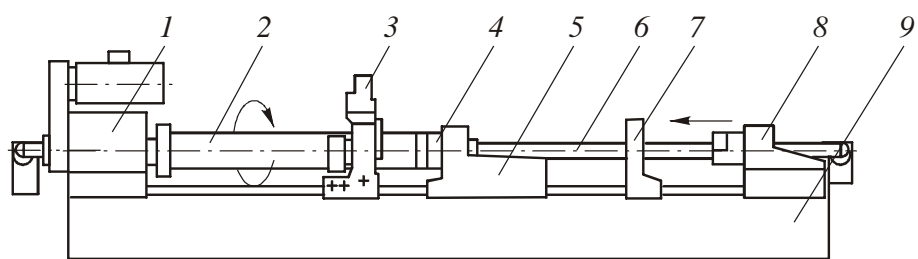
Схема сверления глубоких отверстий сверлом БТА:
